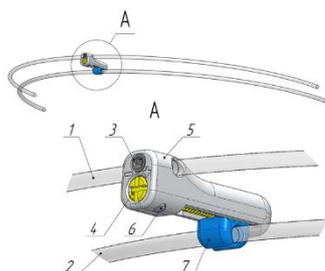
А – регулирующий механизм, 1,2-пластиковые шины, 3-установочный винт, 4-регулирующий винт, 6-штифт, 7-серьга
